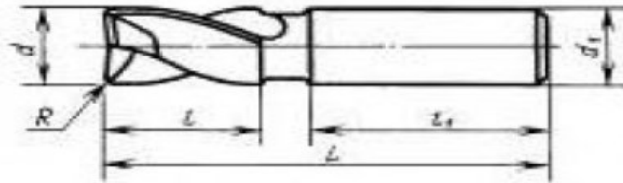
Фреза шпонкова d6P9 2234-0355
